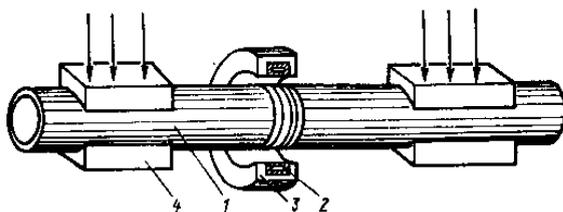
Схема стыковой высокочастотной сварки труб:
